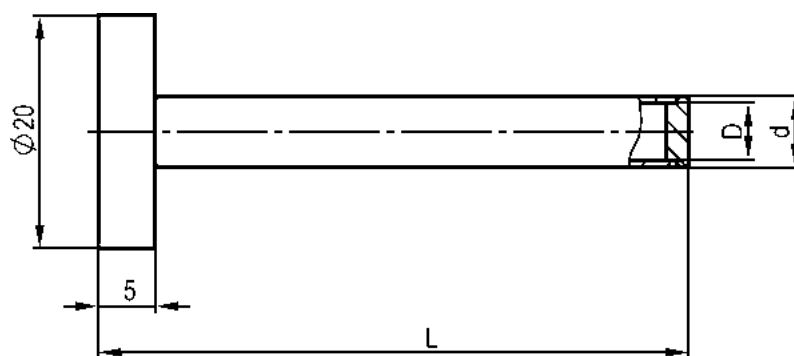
Гильза цилиндрическая сварная с монтажным кольцом OS2
